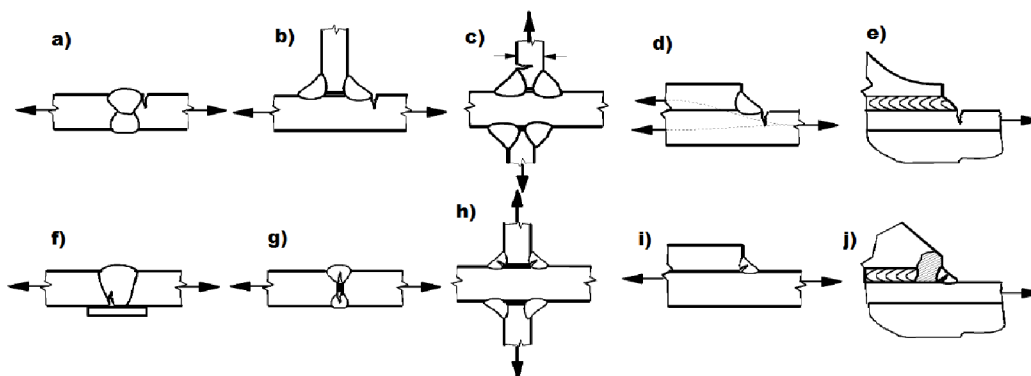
Konstrukční detaily a průběhy napětí[4]
